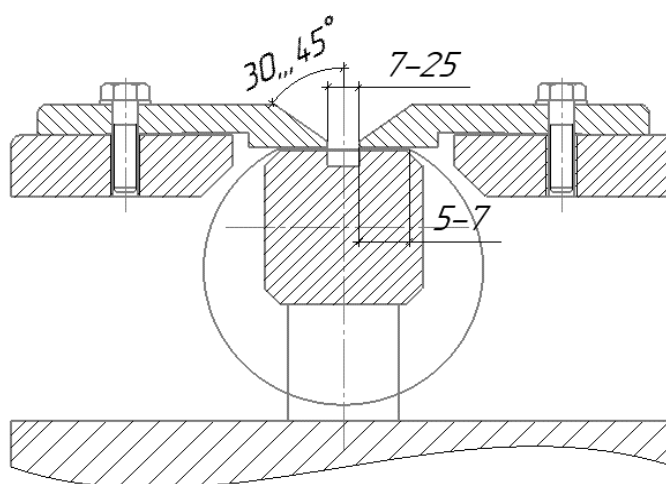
Схема закрепления обечайки при сварке
